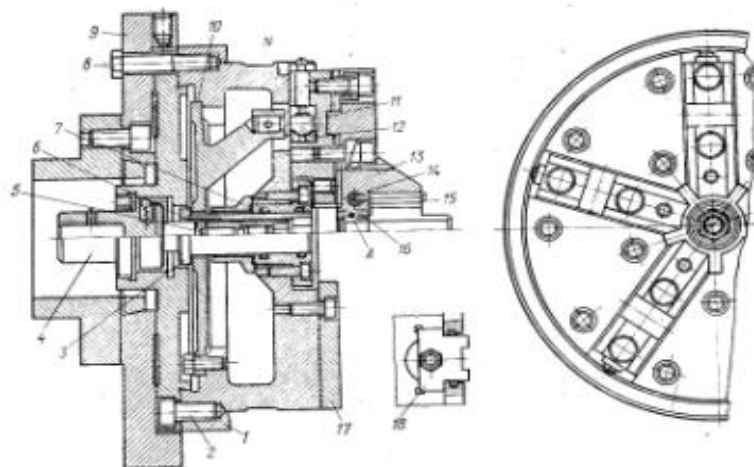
Мембранний патрон для установки і затиску циліндричних зубчастих коліс
